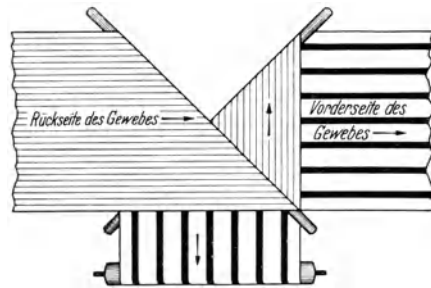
Wendevorrichtung für Gewebe-Schermaschinen. (Parks & Woolson Machine Company Springfield, Vermont.)
